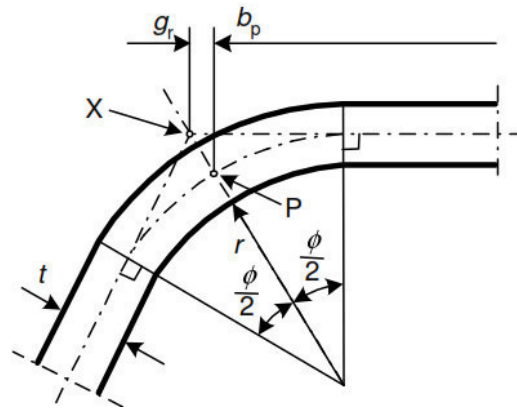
Pormenor da geometria do canto arredondado (EN 1993-1-3, 2006).
